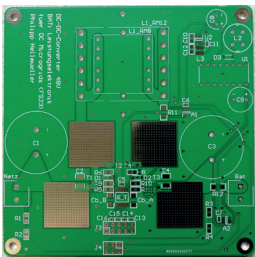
Das unbestückte PCB. Mittig sind die grossen Kühlflächen der MOSFETs ohne Lötstopmmaske ersichtlich.
